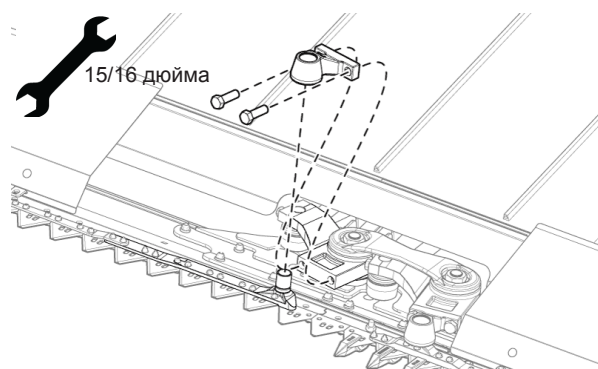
Снятие корпуса подшипников с головки правого ножа.
